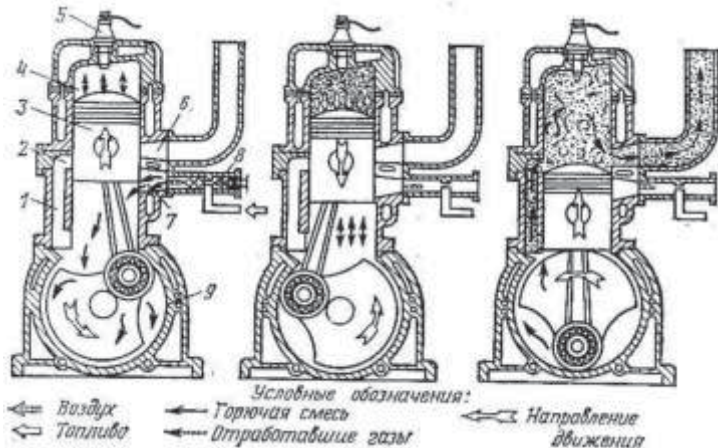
Схема устройства и работы двухтактного двигателя:
